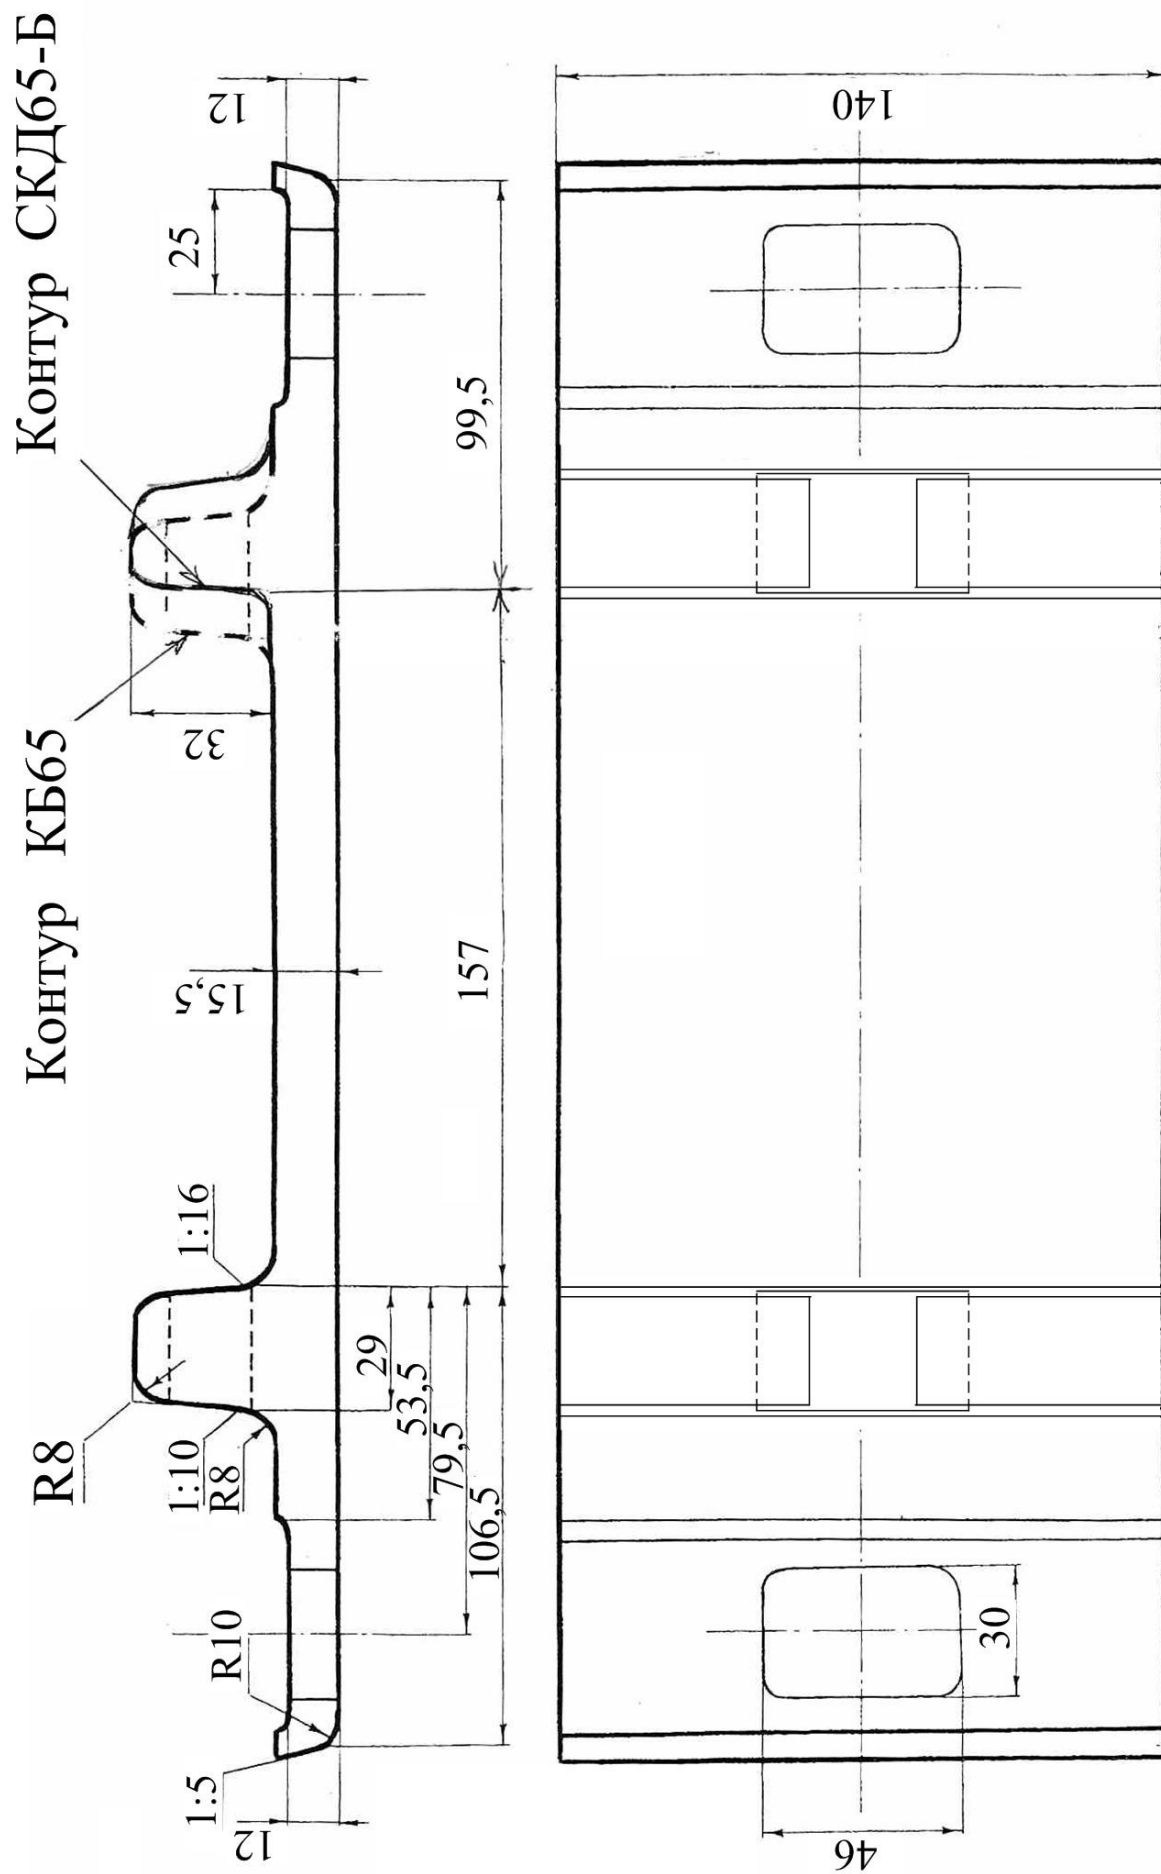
Підкладка роздільного скріплення СКД65-Б
